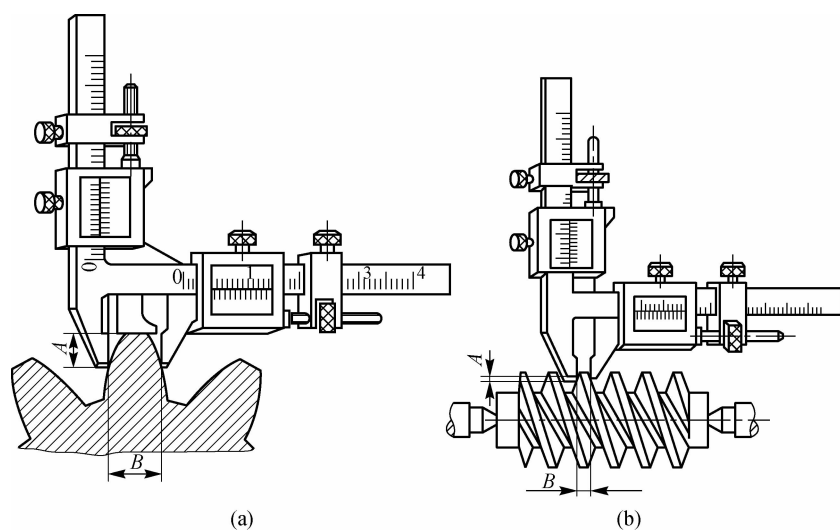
齿厚游标卡尺测量齿轮与蜗杆
